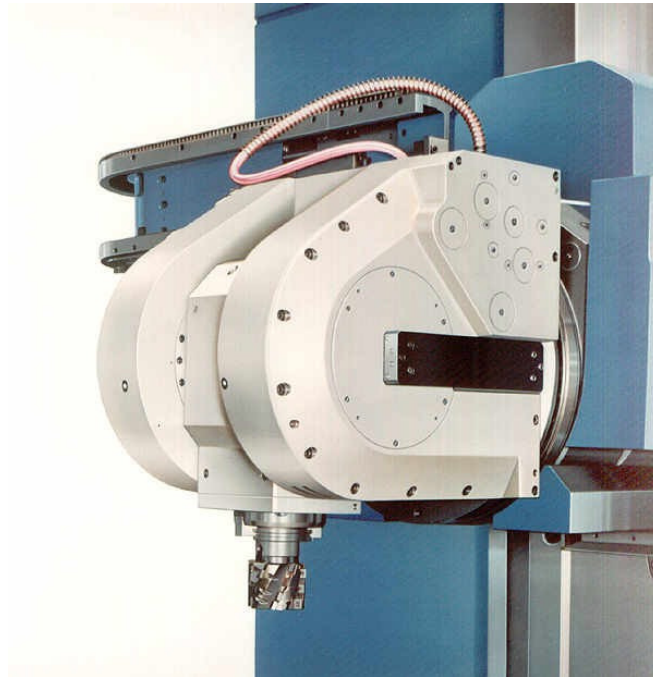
Univerzální automaticky indexovaná frézovací hlava [12]
